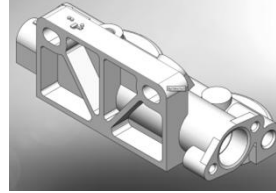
Трехмерная твердотельная модель «Корпус ФТ 040.1117 110»
